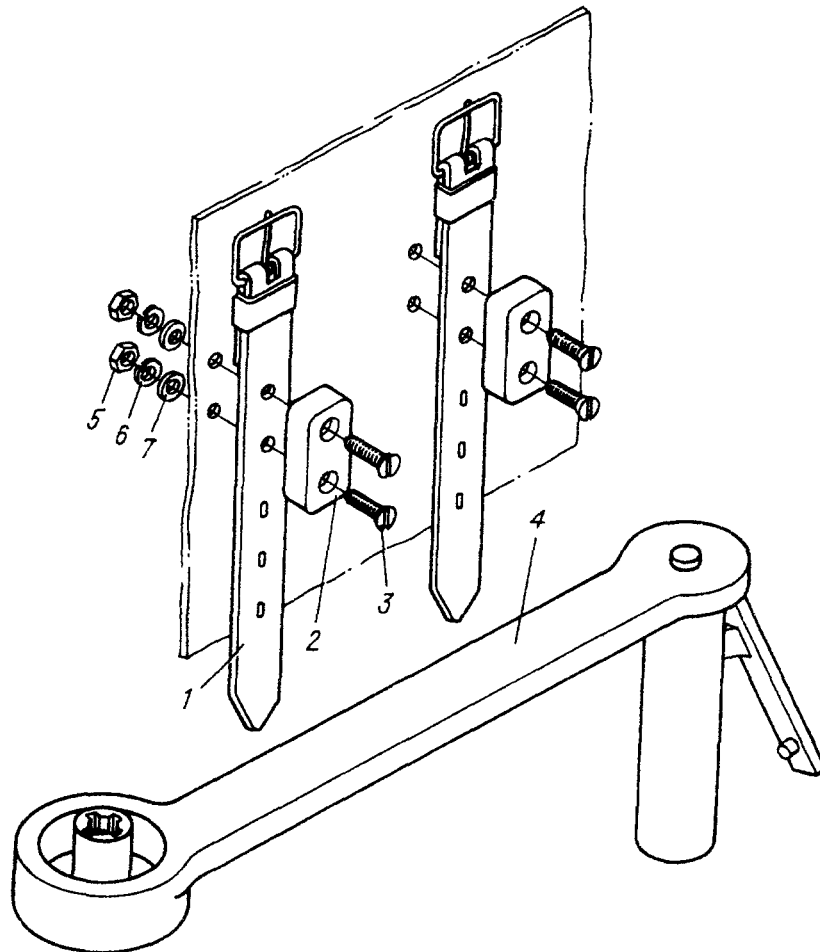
УСТАНОВКА РУЧКИ ПРИВОДА ЛЕБЕДКИ БЛ-56
